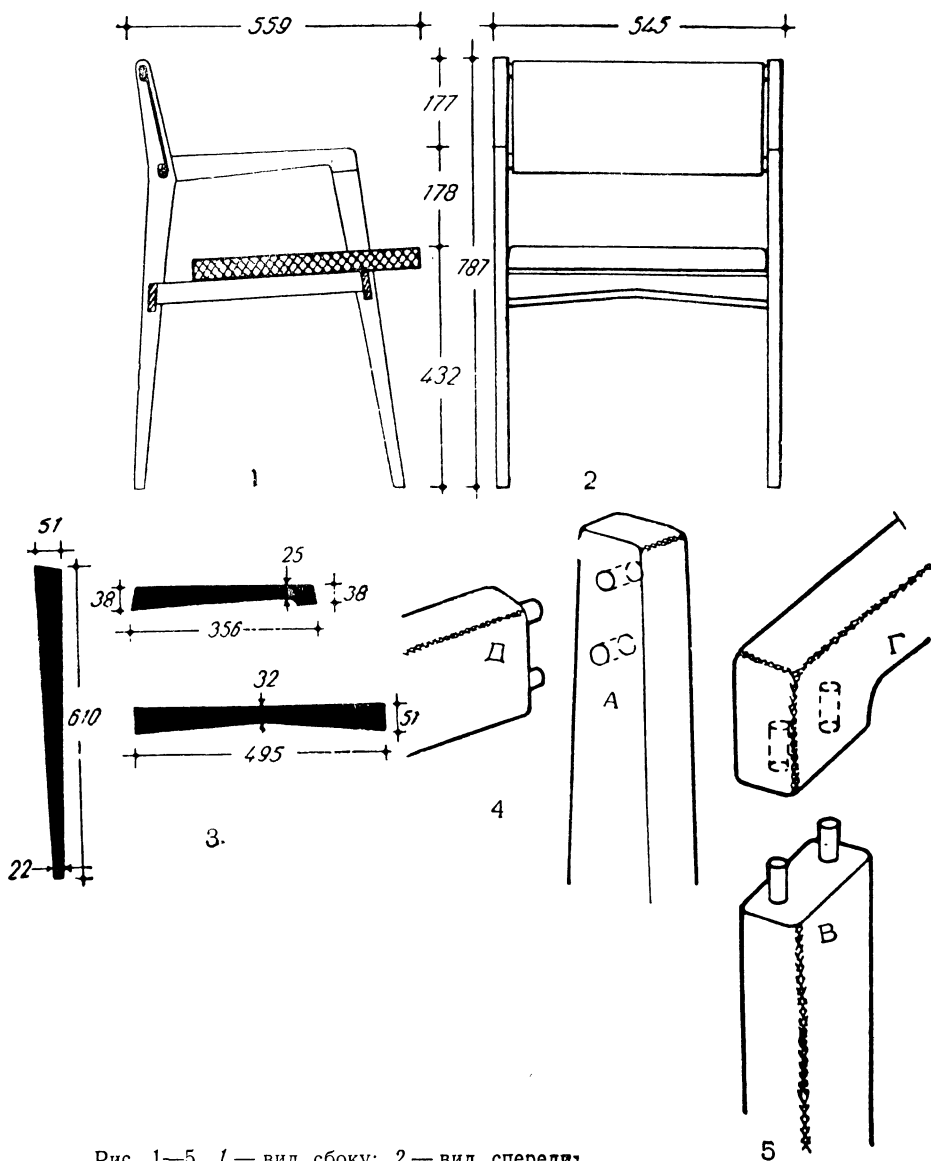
5. 1 — вид сбоку; 2 — вид спереди; 3 — детали ножки, подлокотника и передней царги; 4 — эскиз соединения верхнеспиночного бруса с задней ножкой; 5 — эскиз соединения подлокотника с передней ножкой.
